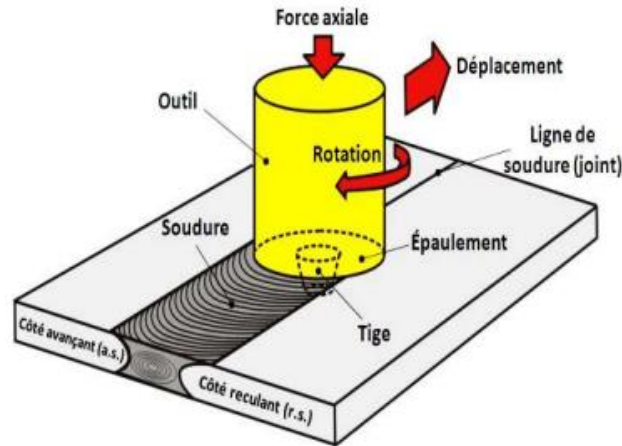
Schéma technique décrivant le mécanisme de soudage par friction malaxage [43]
